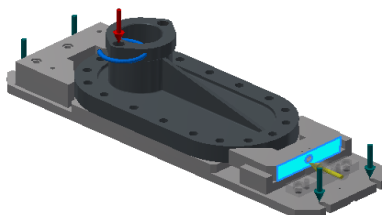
Действие усилия зажима заготовки детали «Опора» в приспособлении
